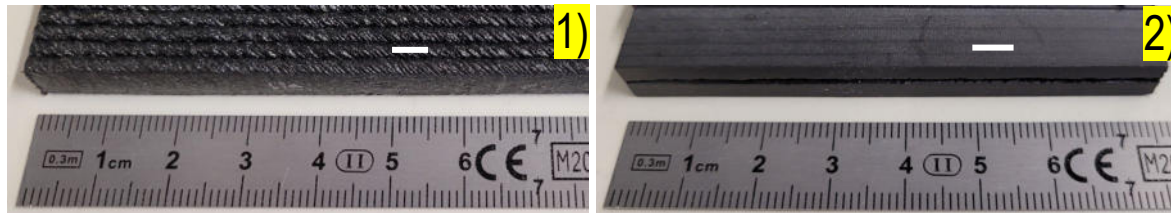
PC-ABS-GF Proben für die WLI-Aufnahmen; 1): unbearbeitet; 2): gefräst
